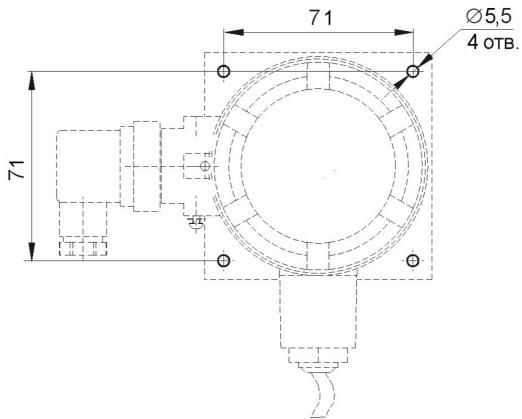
Монтажные размеры корпуса измерительного преобразователя ИТ-2ЦМ.ВИ
